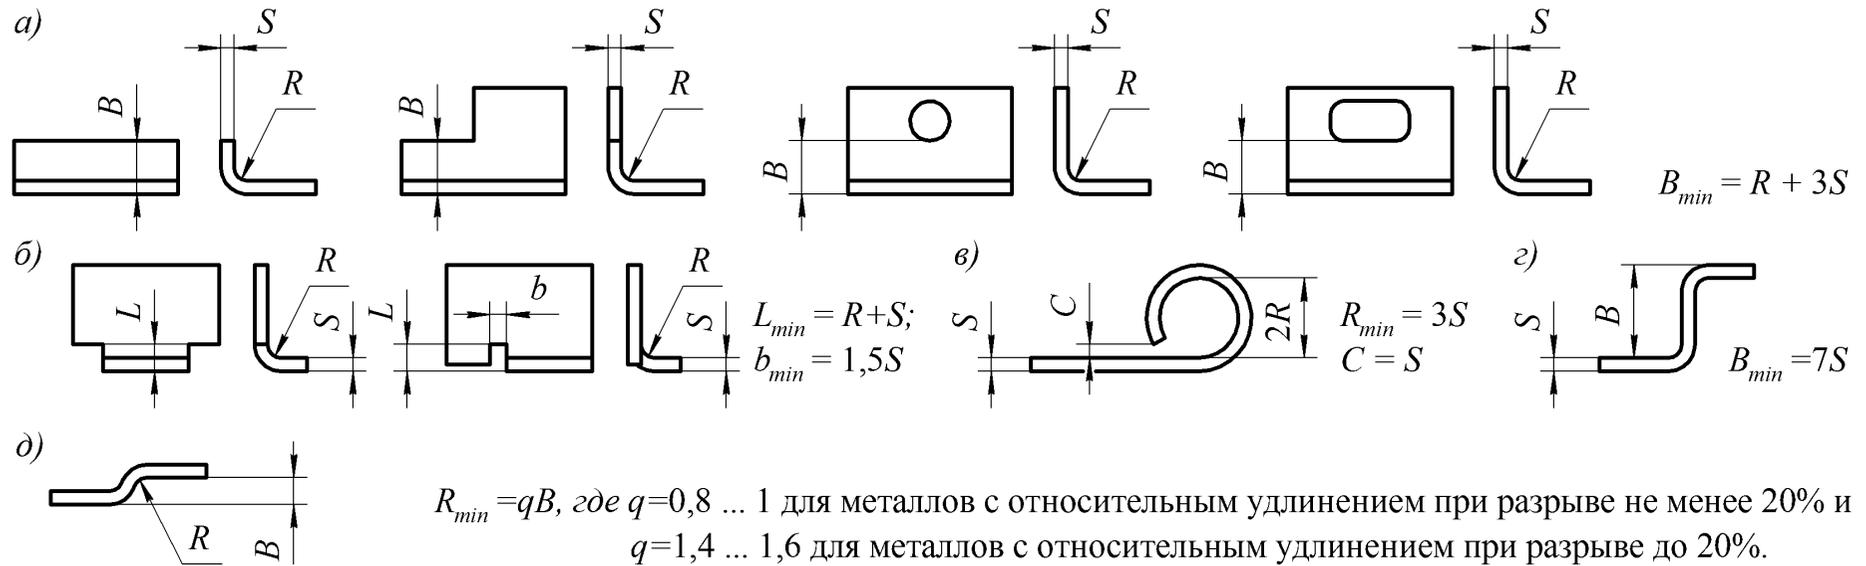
Рекомендуемые размеры элементов деталей, изготавливаемых гибкой из листовых заготовок, [25]
